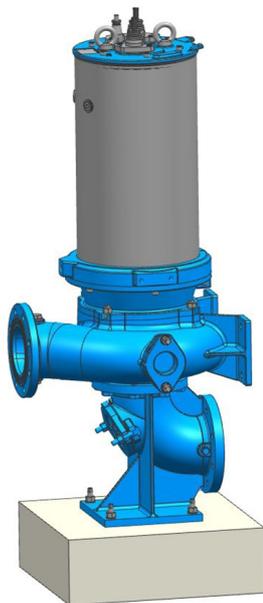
Trockenaufstellung Vertikal; bis Einpass 315 auf Einlaufkrümmer; stationär
